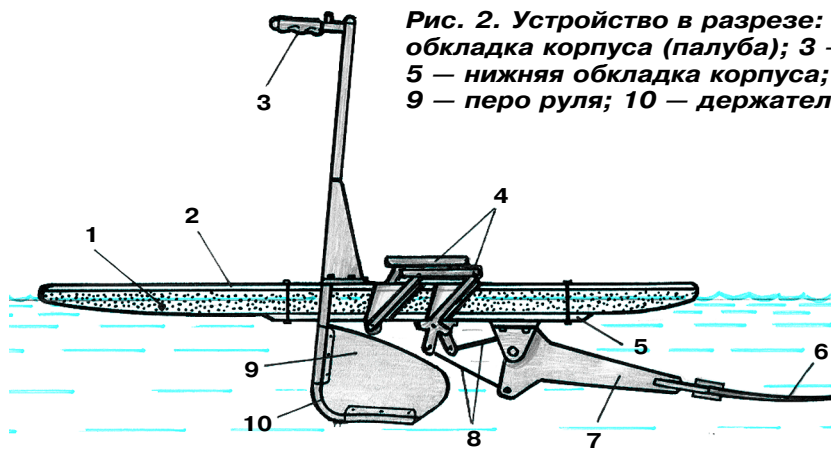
Устройство в разрезе: 1 — пенопластовый корпус; 2 — верхняя обкладка корпуса (палуба); 3 — ручки рулевого управления; 4 — педали; 5 — нижняя обкладка корпуса; 6 — ласта; 7 — маятник; 8 — тяги привода; 9 — перо руля; 10 — держатель пера руля.
